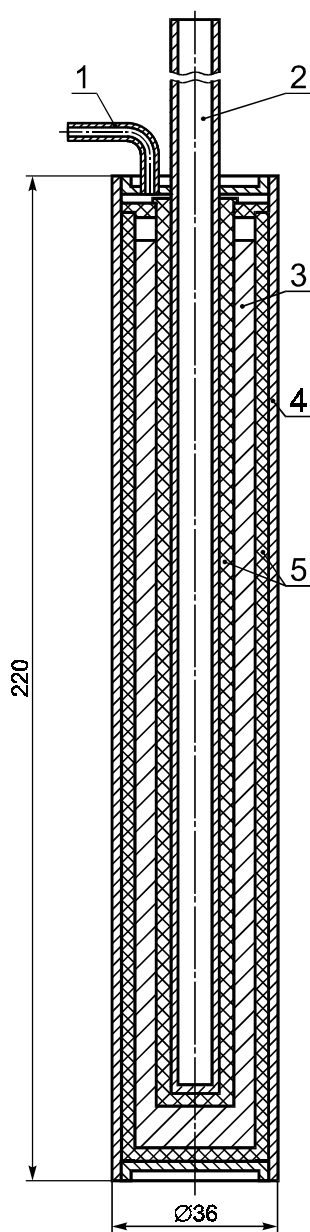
Схема реперной точки производства НПП «Элемер»: 1 — трубка для откачки; 2 — нержавеющая трубка; 3 — металлический образец; 4 — нержавеющая труба; 5 — графитовый стакан
